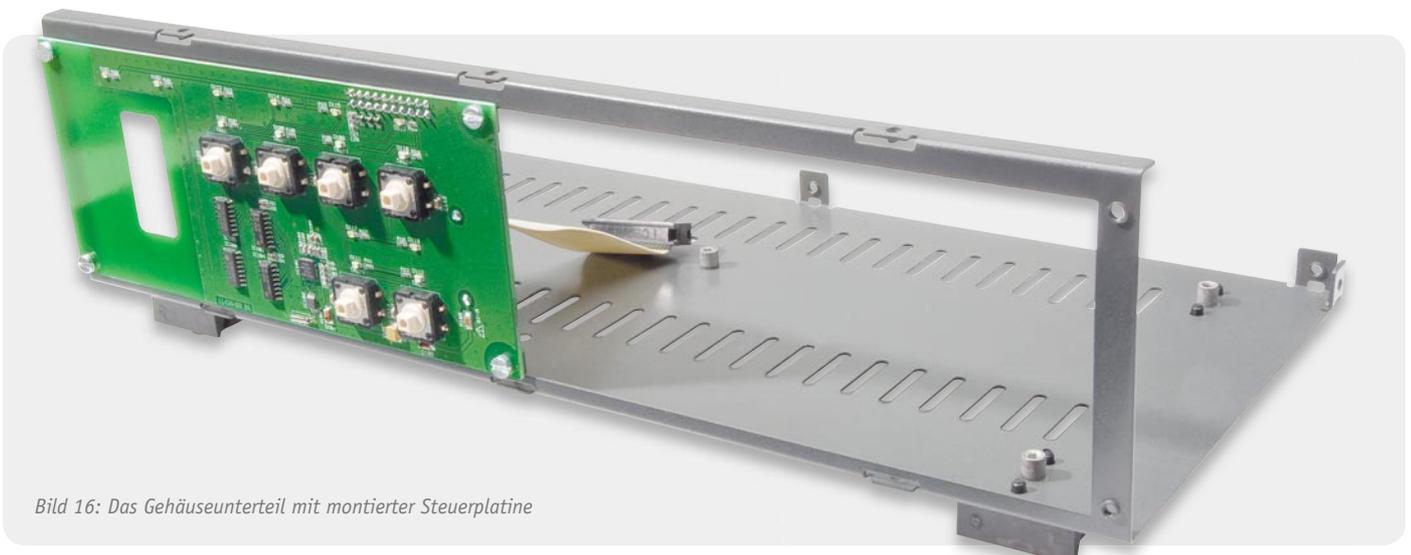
Das Gehäuseunterteil mit montierter Steuerplatine
